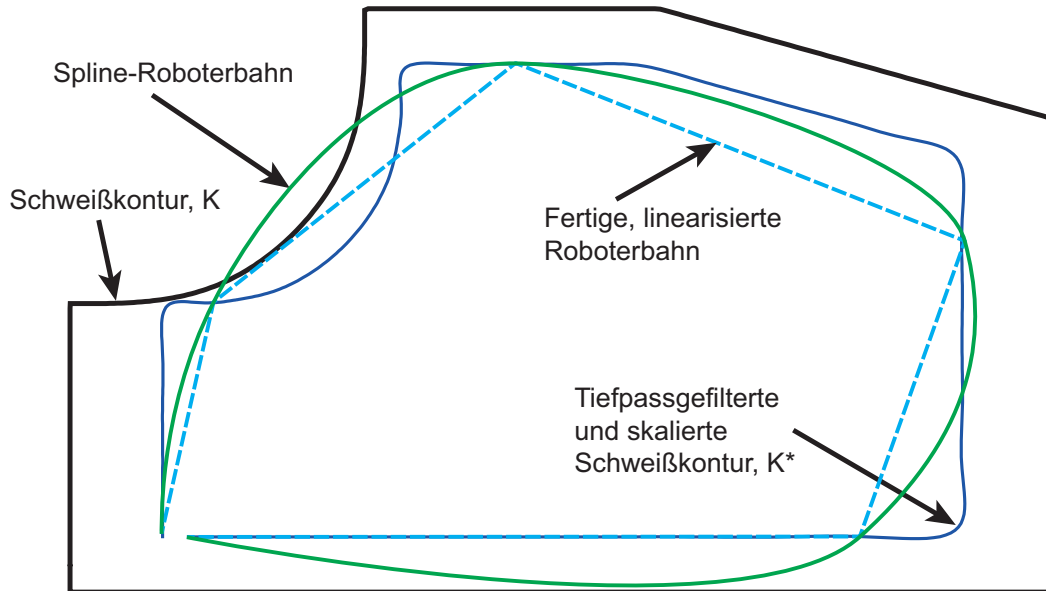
Berechnete Roboterbahn zur Bearbeitung der großen, umlaufenden Schweißnaht der LKW-Türe
